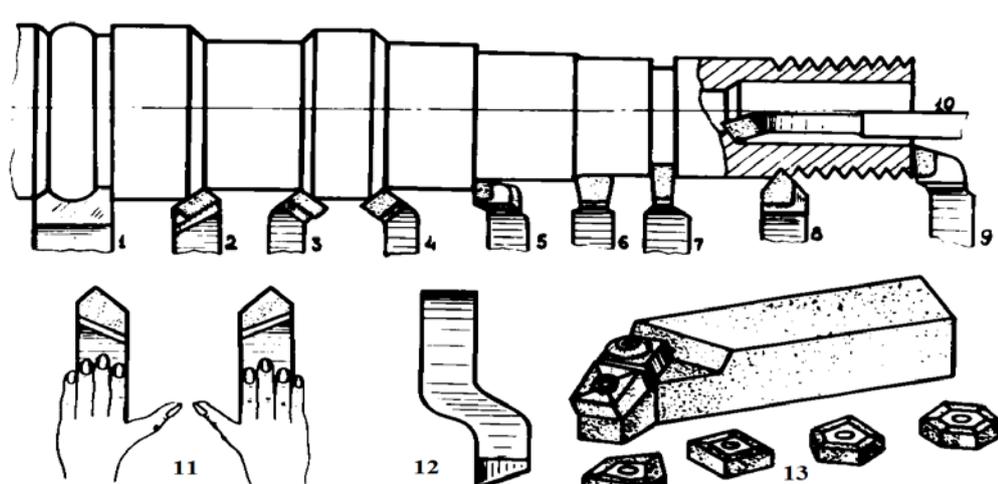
Типы токарных резцов: 1 – фасонный; 2 – прямой проходной; 3 - 5 – отогнутые проходные; 6 – чистовой; 7 – отрезной; 8 – резьбовой; 9 – подрезной; 10 – расточной; 12 – строгальный; 13 – сборный со сменными пластинками
